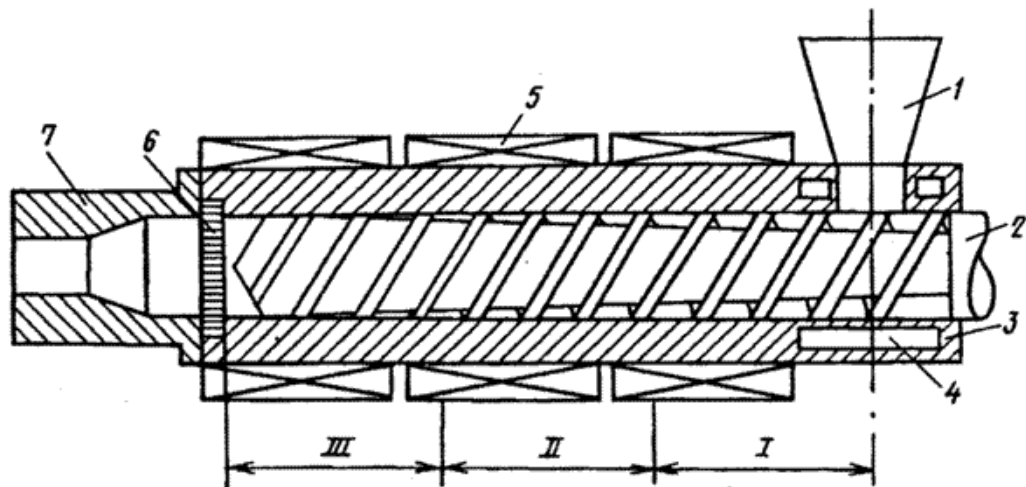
Схема одношнекового екструдера: 1- бункер; 2- шнек; 3- циліндр; 4- порожнина для циркуляції води; 5- нагрівач; 6- решітка з сітками; 7- формуюча головка [13].
